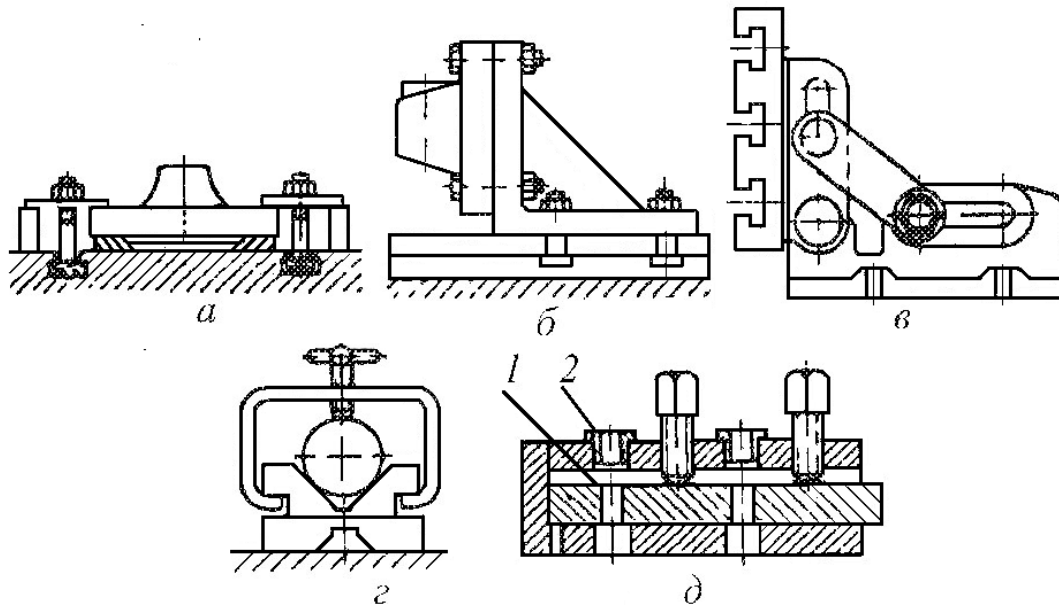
Пристрої для установки заготовок на свердильних верстатах
